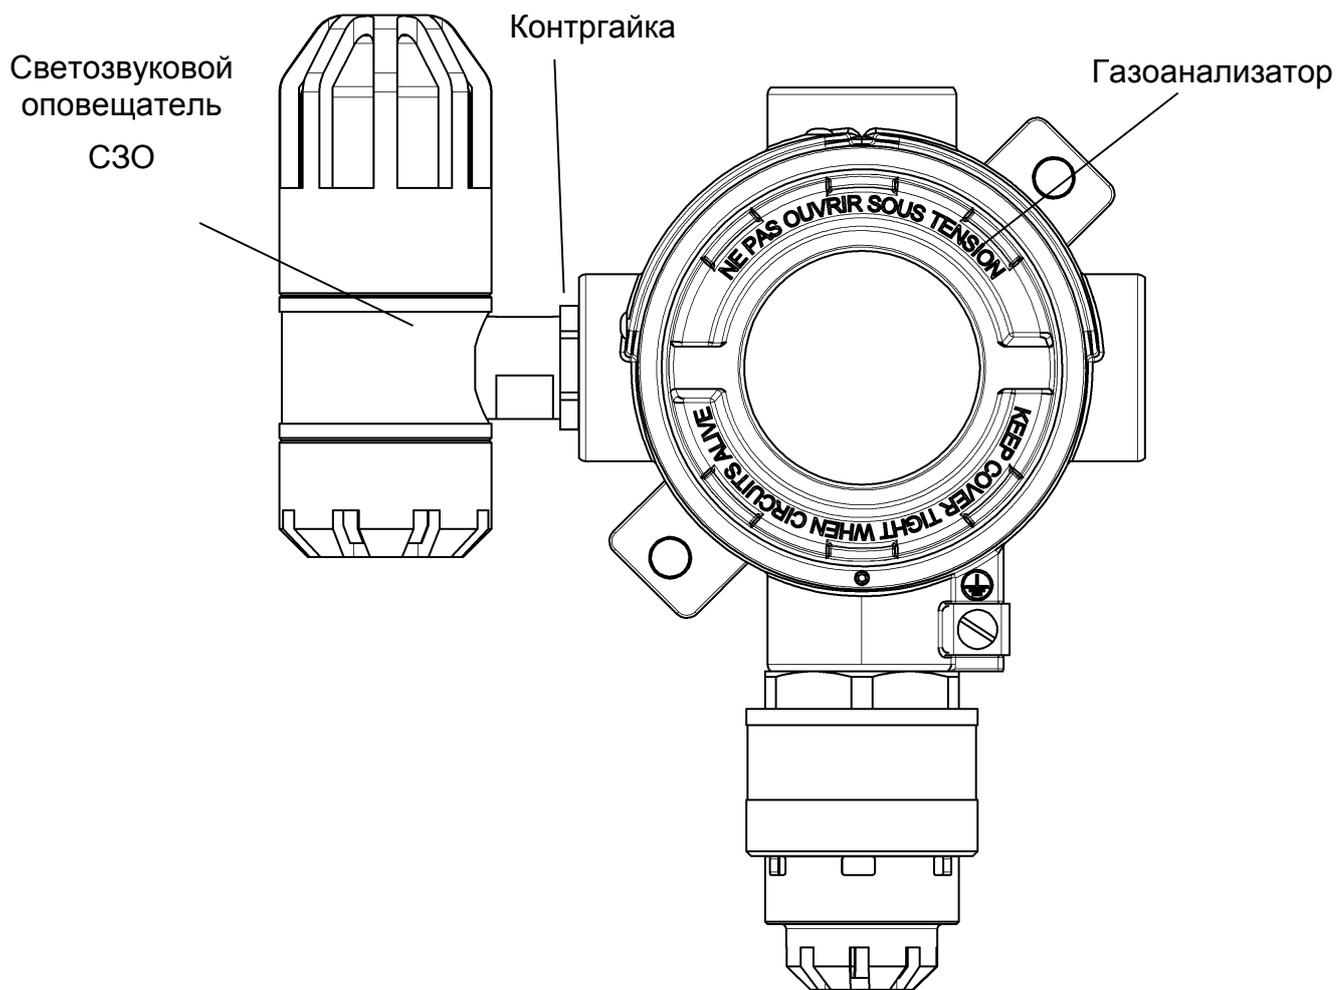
Внешний вид газоанализатора со светозвуковым оповещателем
